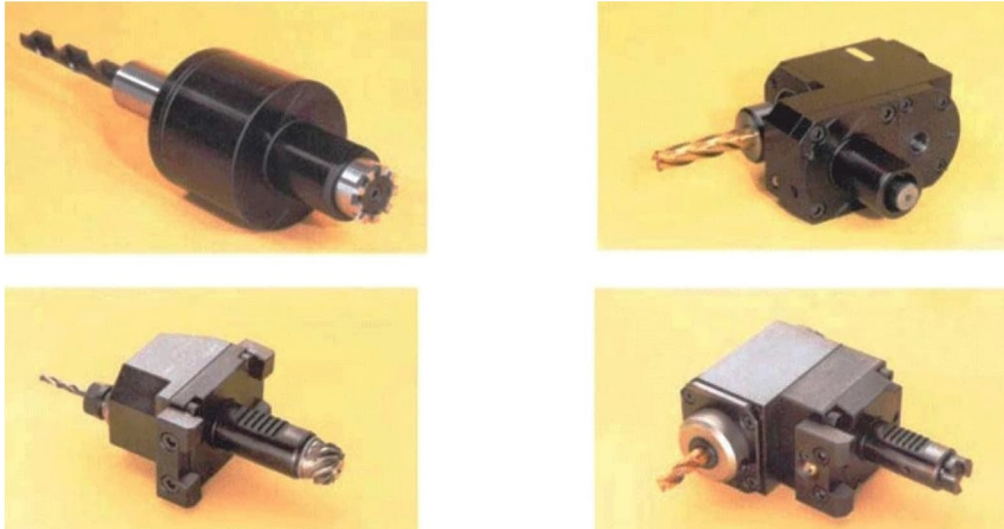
Приводний інструмент для верстатів токарної групи з ЧПК
